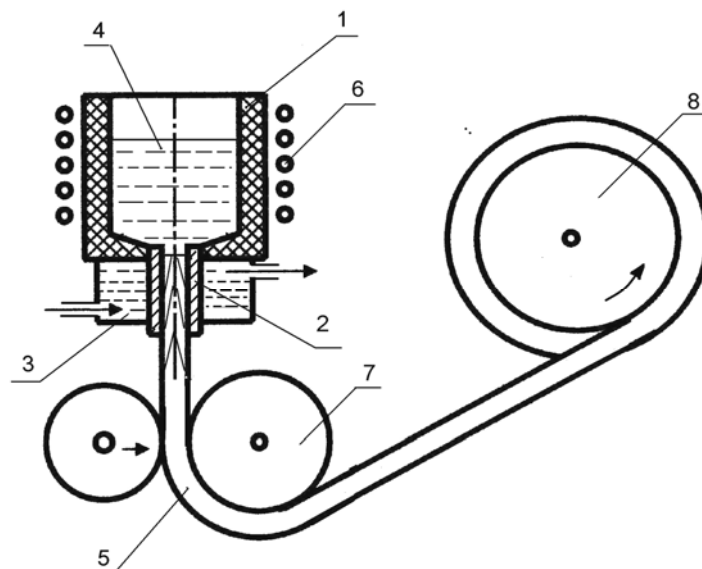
Схема установки для одержання безперервнолитої бронзової заготовки для підшипників ковзання
